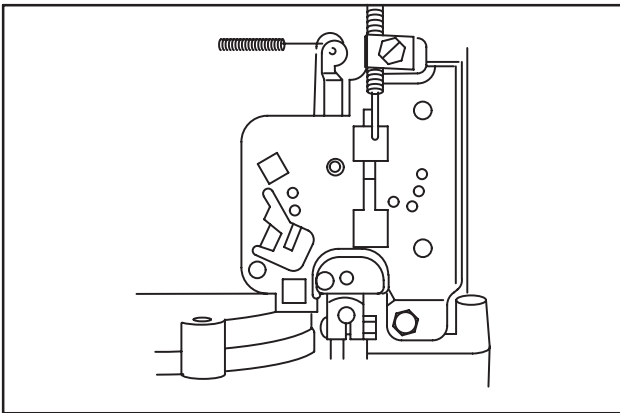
170700, 190700, 191700, 192700, 193700, 194700, 195700, 196700, 220700, 252700, 253700, 254700, 257700, 256700, 258700, 280700, 28A700, 28B700, 28C700, 28D700, 28M700, 283700, 286700, 289700 avec commande à crémaillère verticale pour carburateurs LMT Briggs & Stratton/Walbro
